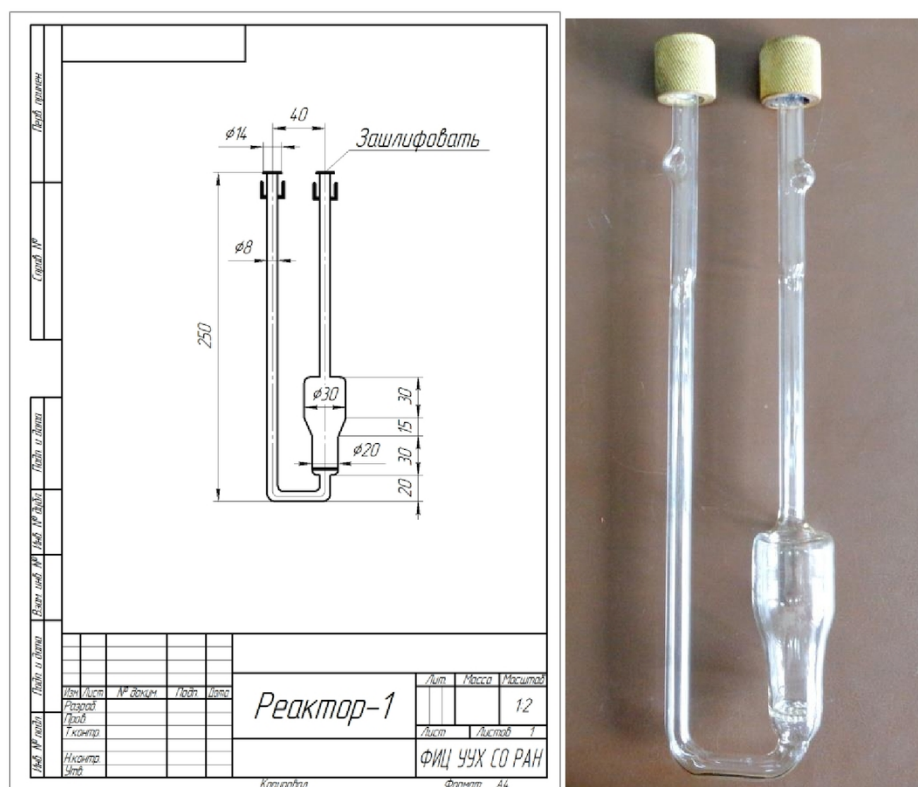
Чертеж и внешний вид кварцевого реактора с виброожиженным слоем катализатора (реактор-1).
